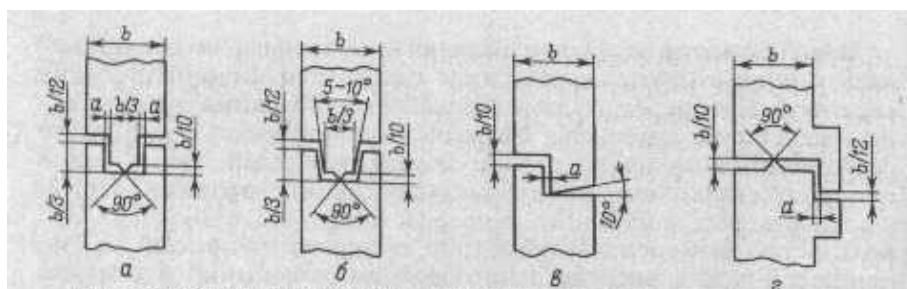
Конструкции кромок стыкуемых деталей при сварке жестких пластмасс;  $a = 0.1$  мм. Пояснения в тексте
